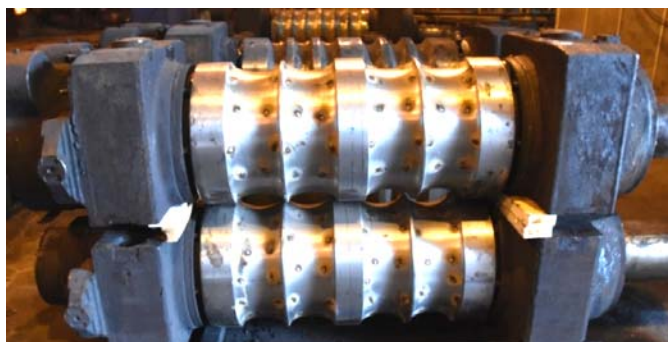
Валковый блок клетки № 1 стана 320 с нанесенной сварочной шагренью
